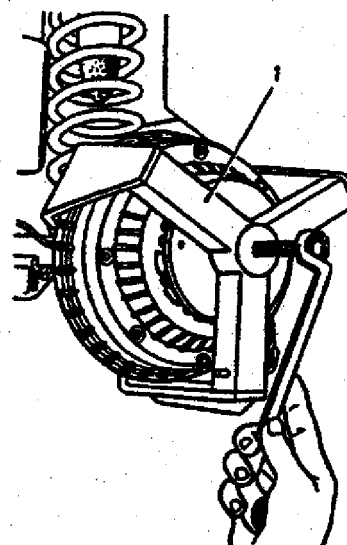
Remoção do tambor: 1 - extrator 67.7823-9519.
